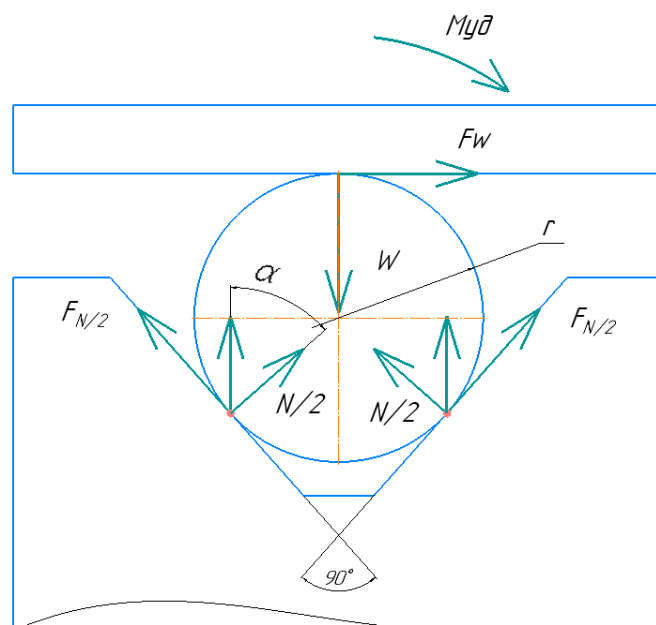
Силы, возникающие при закреплении заготовки в приспособлении
